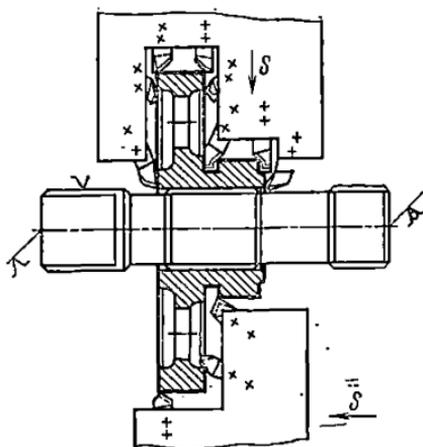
Наладка многорезцового токарного полуавтомата для обработки заготовки зубчатого колеса.
